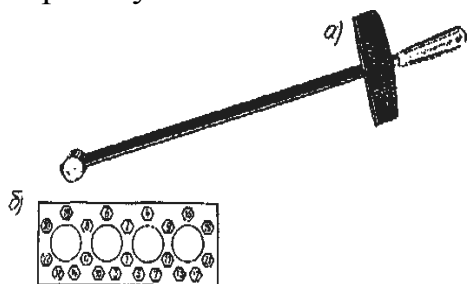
Динамометрична рукоятка мод. 131М: а – загальний вид рукоятки; б - порядок затягування болтів
